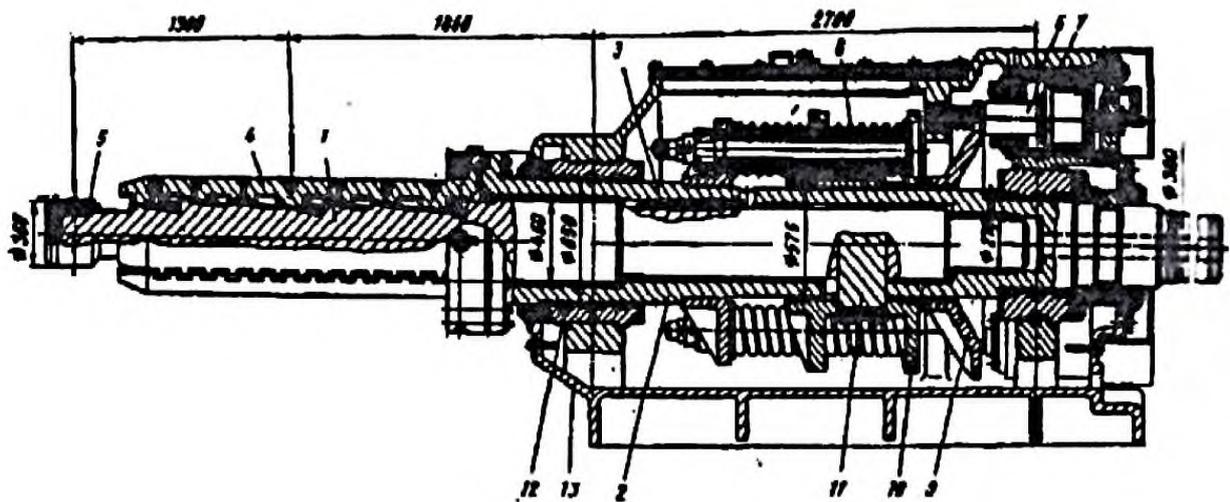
Намоточно-натяжная полосовая моталка с безредукторным приводом [4]
